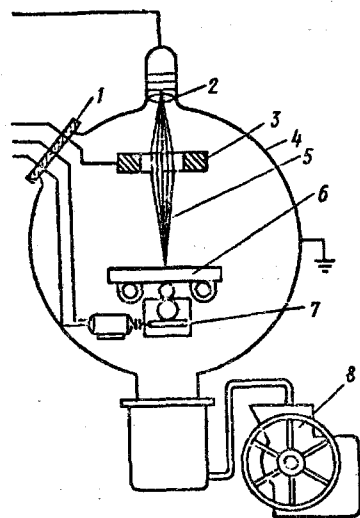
Электронно-лучевая сварка: 1 — электрический вакуумный ввод; 2 — электронная пушка; 3 — электромагнитная фокусирующая линза; 4 — вакуумная камера; 5 — электронный луч; 6 — свариваемое изделие; 7 — механизм перемещения изделия; 8 — вакуумный насос
